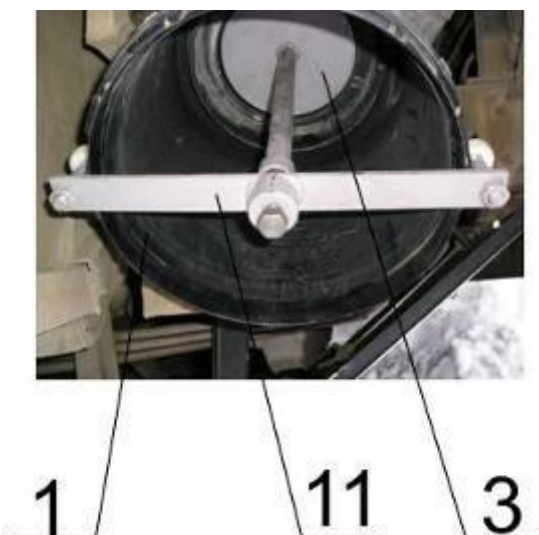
Установка приспособления для проверки герметичности впускного тракта с заглушкой БГВТ 05.000
